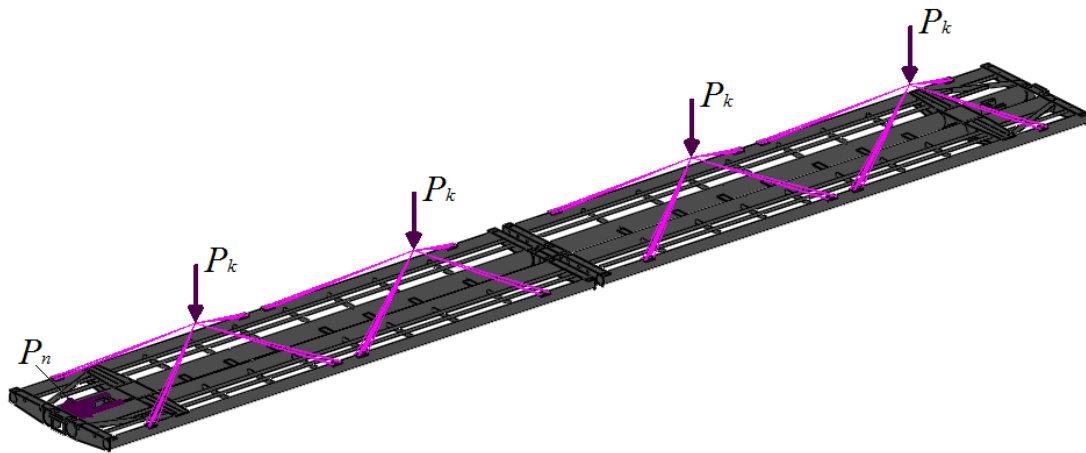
Розрахункова схема несучої конструкції вагона-платформи зчленованого типу
